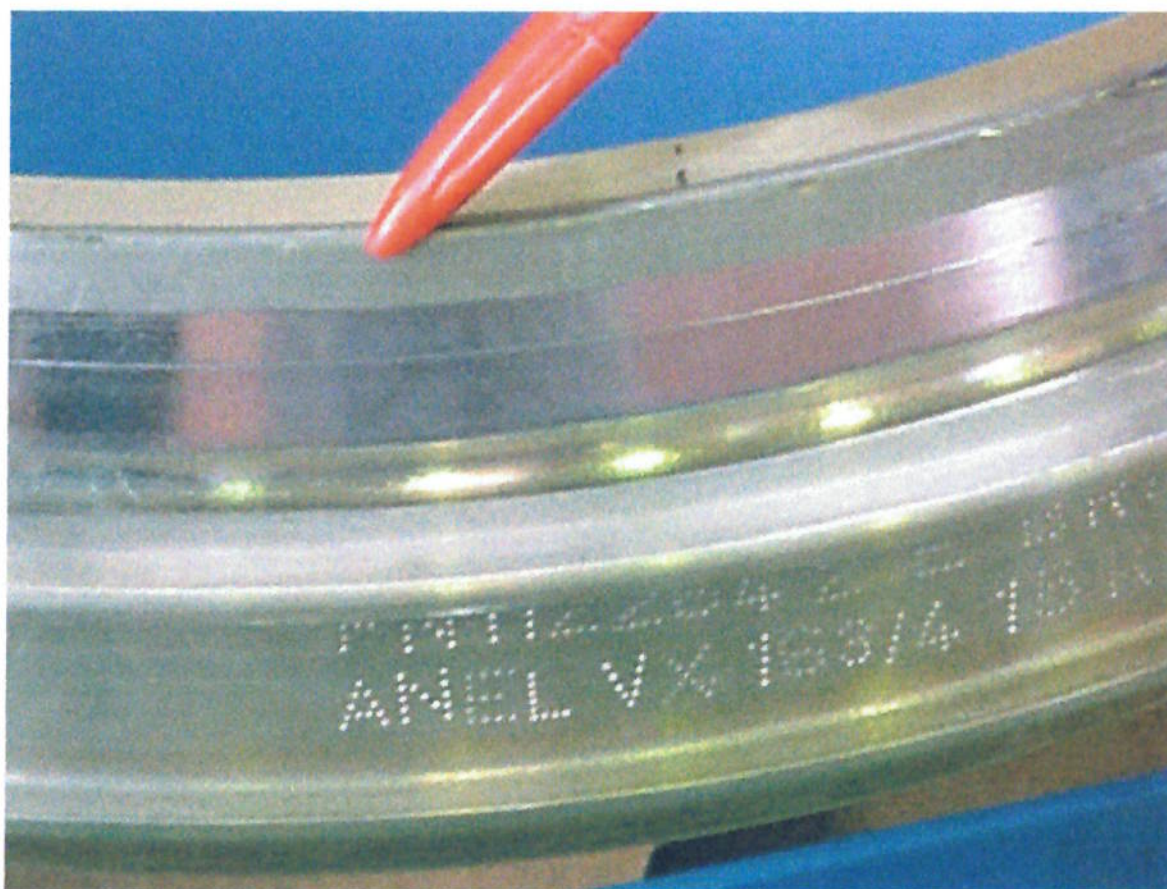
Detalhe de um anel VX 16 3/4" após desmontagem
